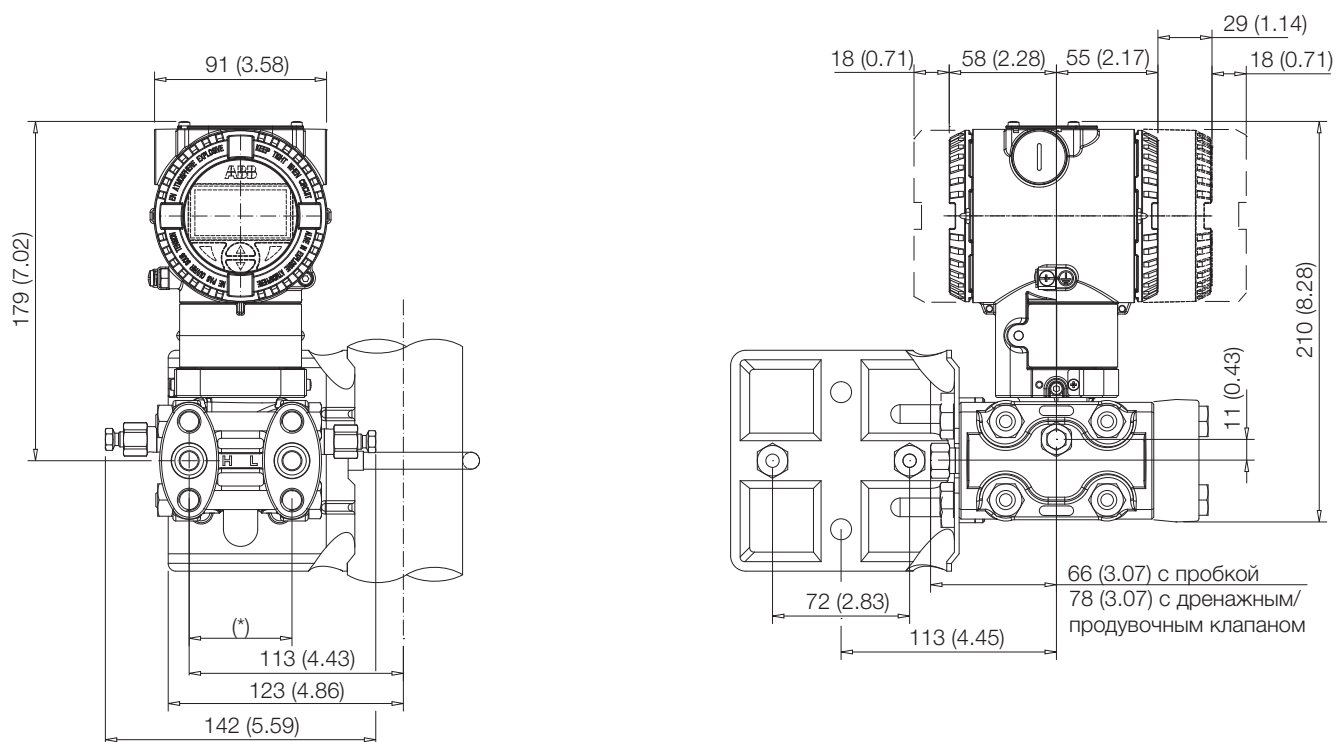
Преобразователь разности давления с цилиндрическим корпусом, установленный на вертикальной трубе с помощью монтажного кронштейна (B2)
